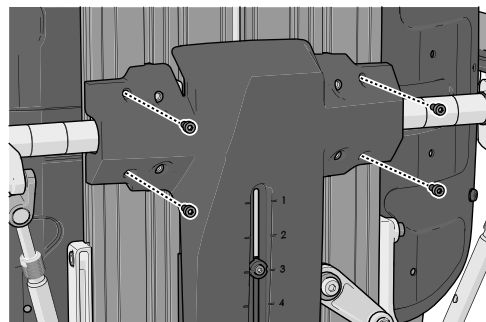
Die Anbringensorte der vier Schrauben, die die Kunststoffabdeckung sichern.
